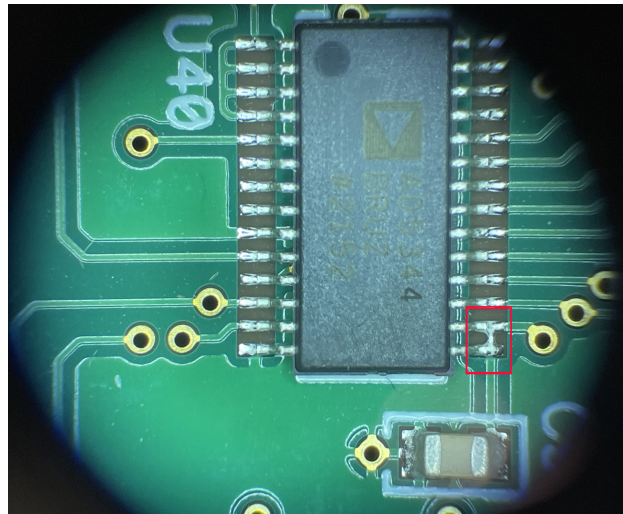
PCB 98 L con fallo por bolas de soldadura.
